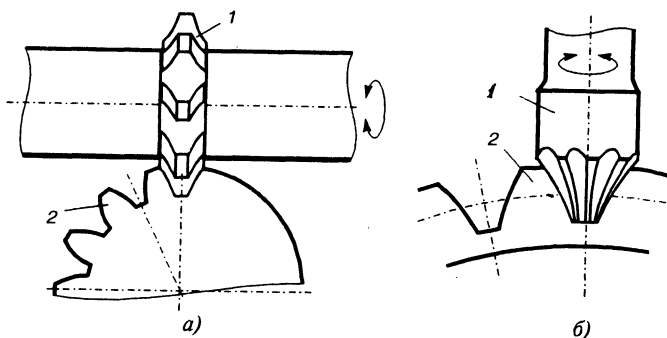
Схема нарезания зубчатых колес фрезой методом копирования:
